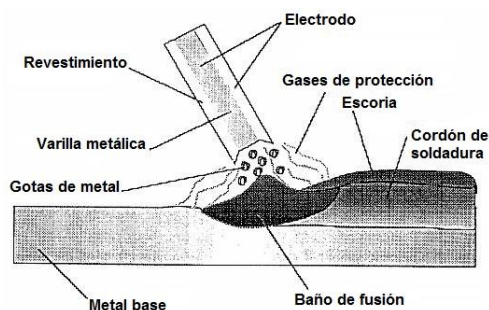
Elementos Principales de la Soldadura SMAW
